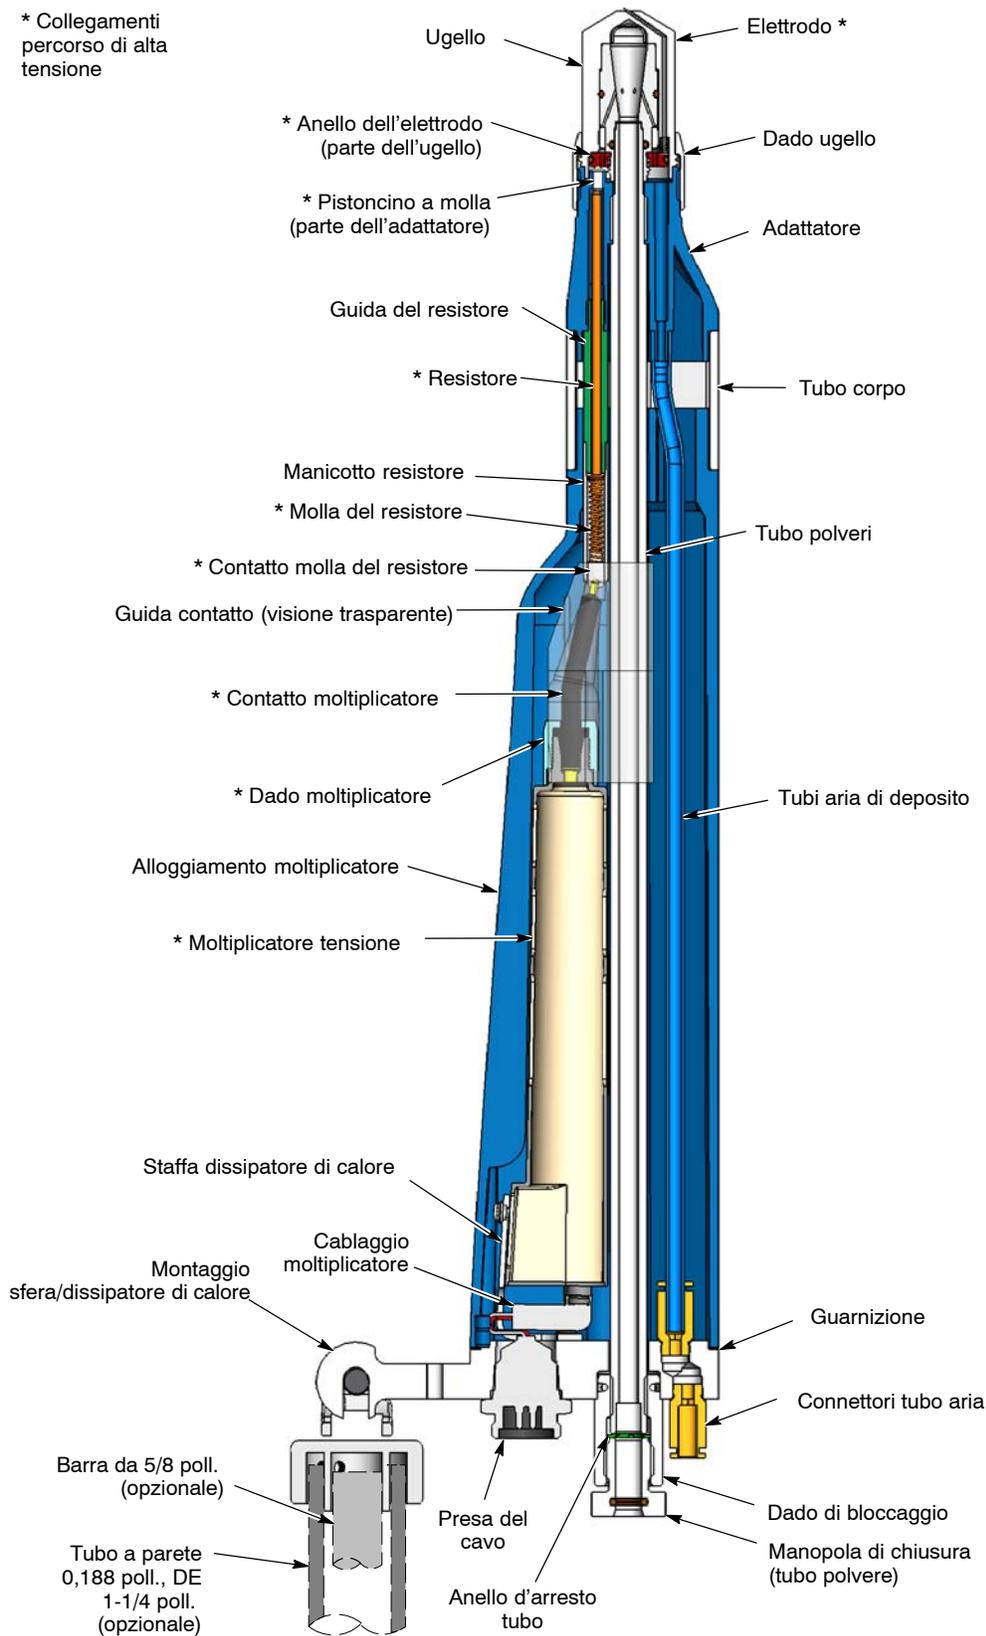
Immagine in sezione - Gruppo e componenti della pistola con montaggio su barra
